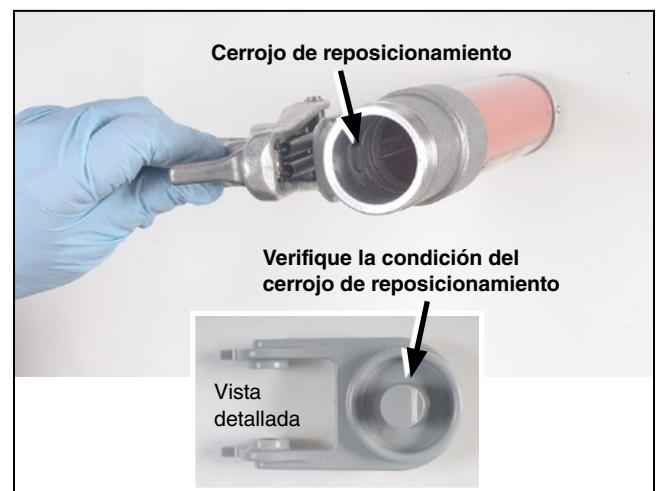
Inspeccione el cerrojo de reposicionamiento.
